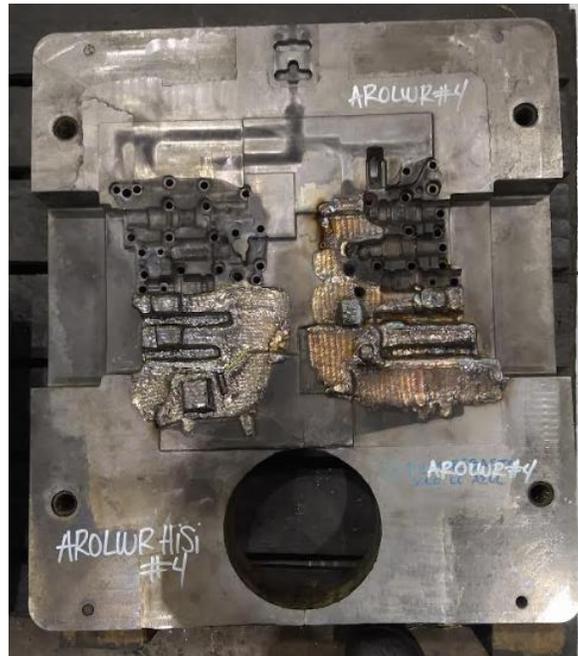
3 Impresión del molde fijo del modelo Aro Lower Fuente: JMEX
